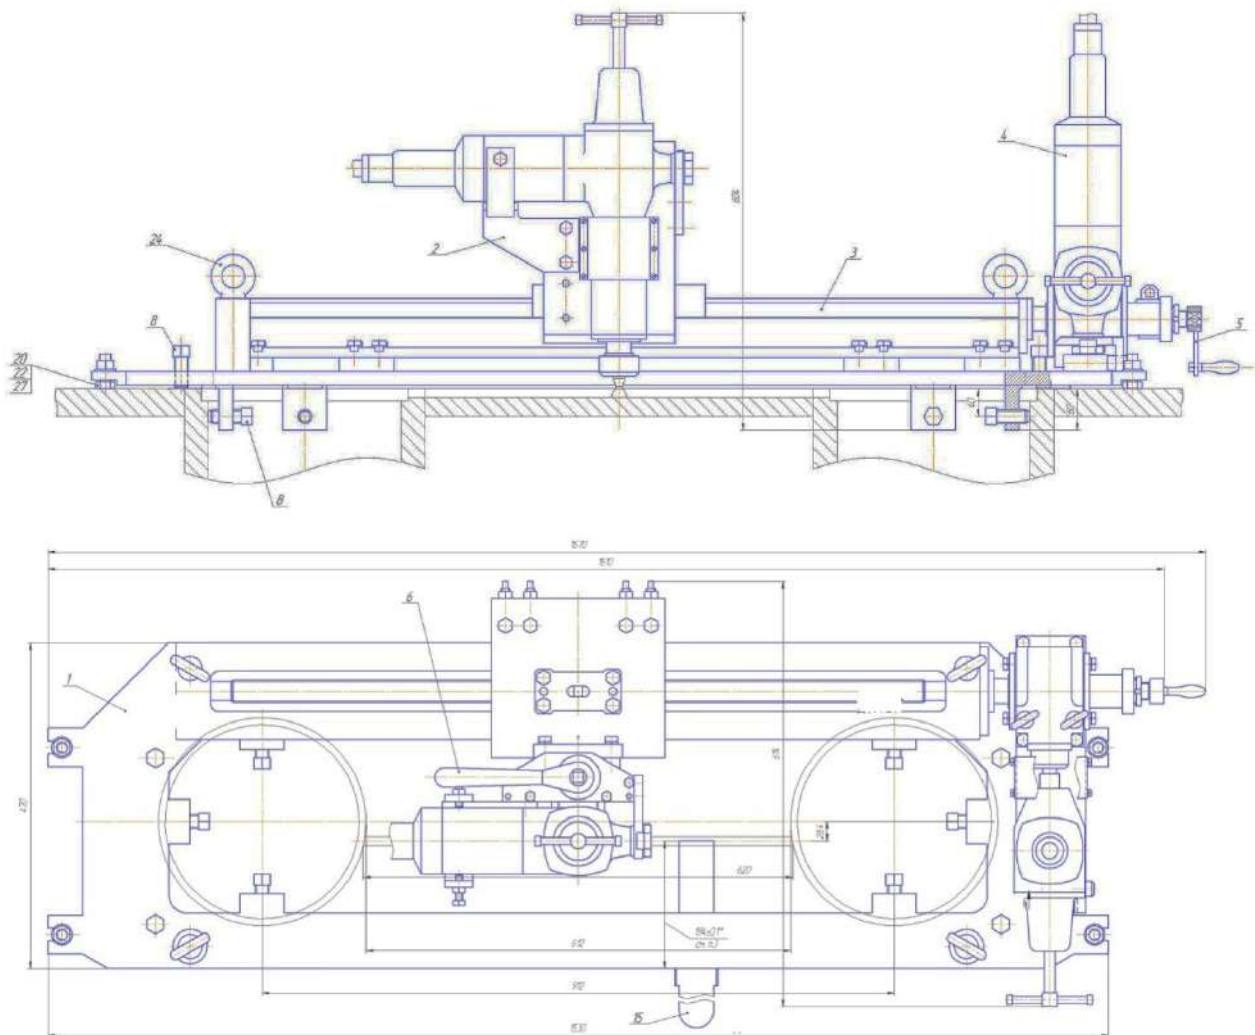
Компоновання мобільного портативного фрезерного верстата
